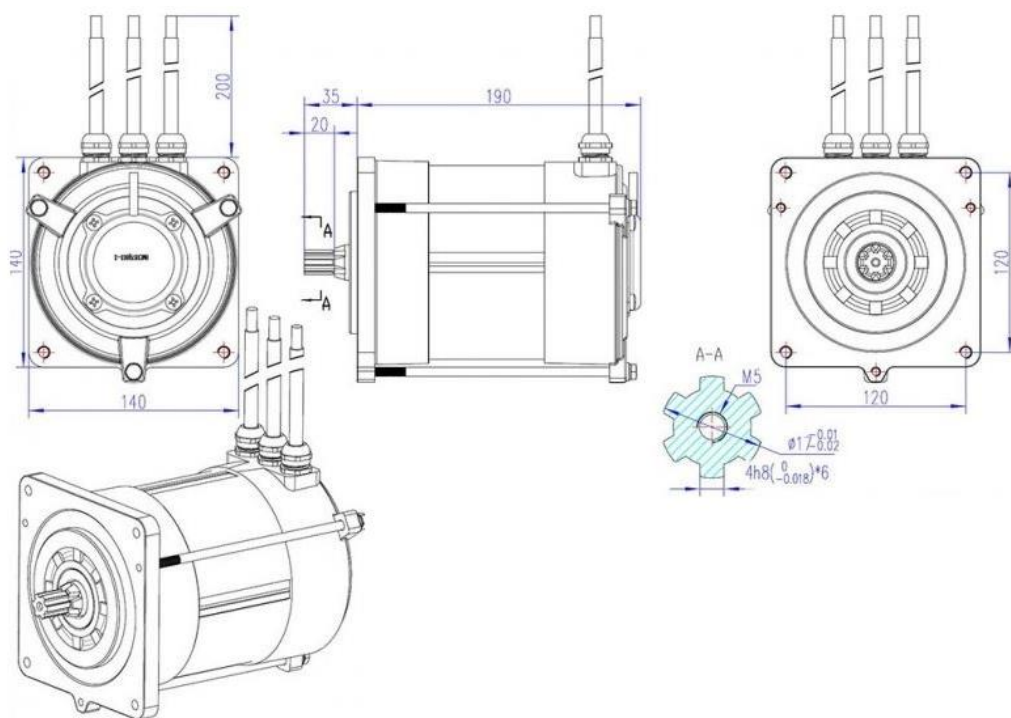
Габаритные размеры электродвигателя Denzel DA90-4.1
